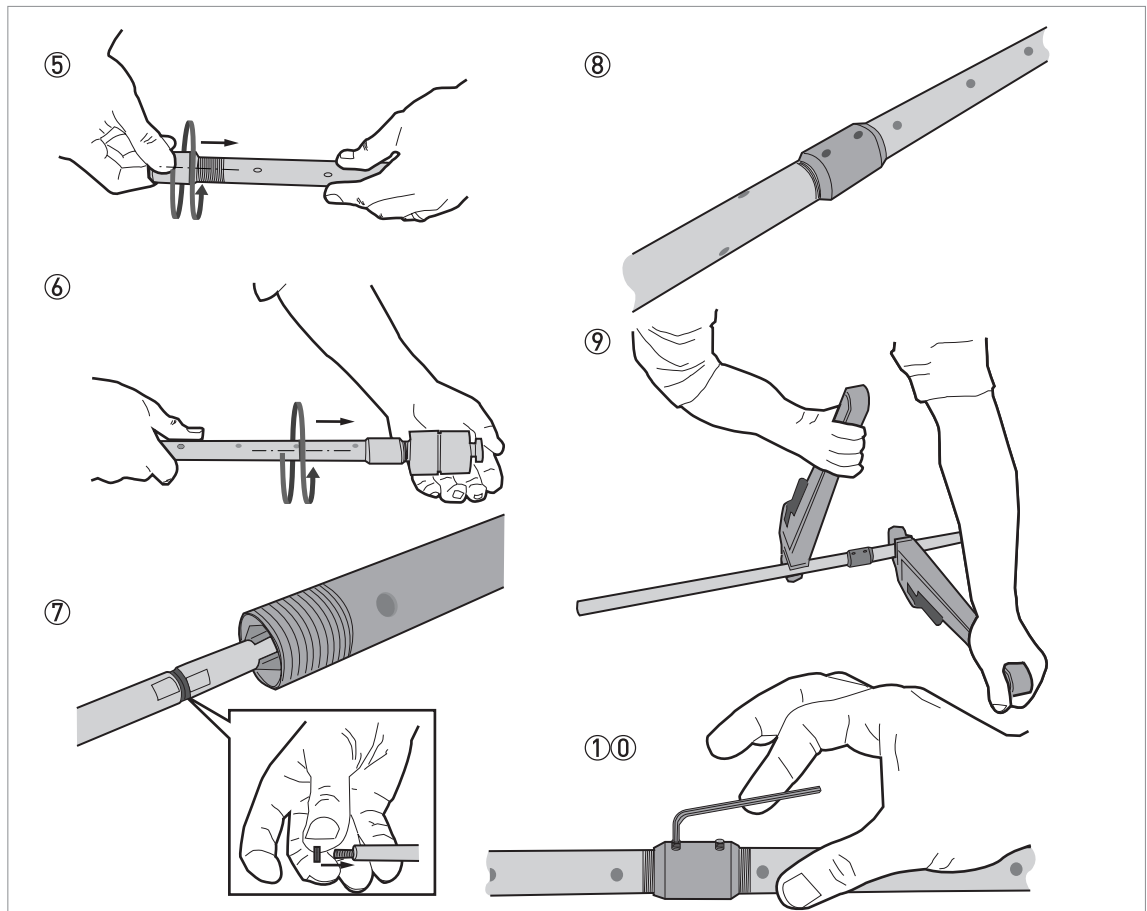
Como montar a sonda coaxial segmentada: parte 2
